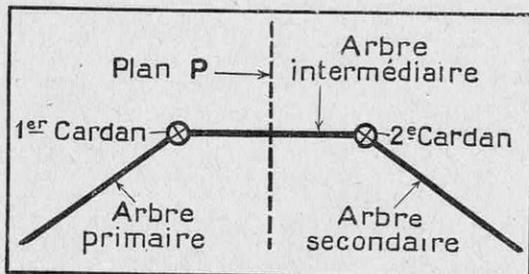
LE JOINT DE HOOKE OU DOUBLE CARDAN
